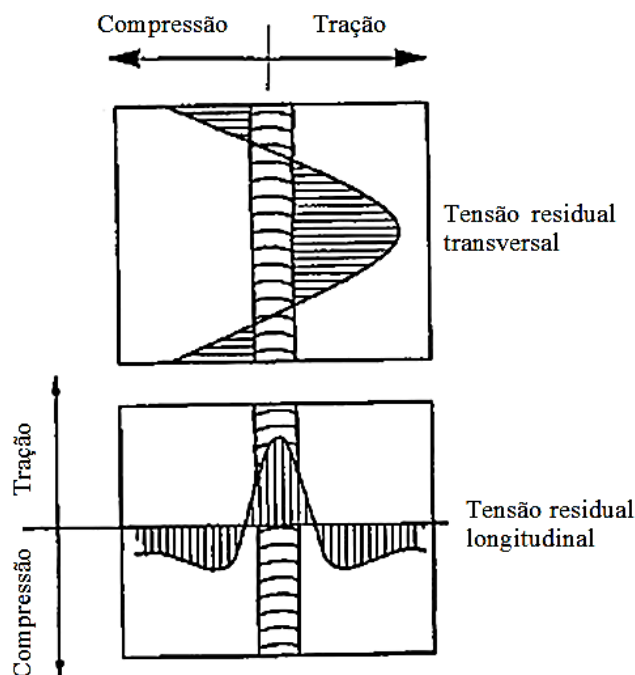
Tensões residuais devido ao processo de soldagem.
